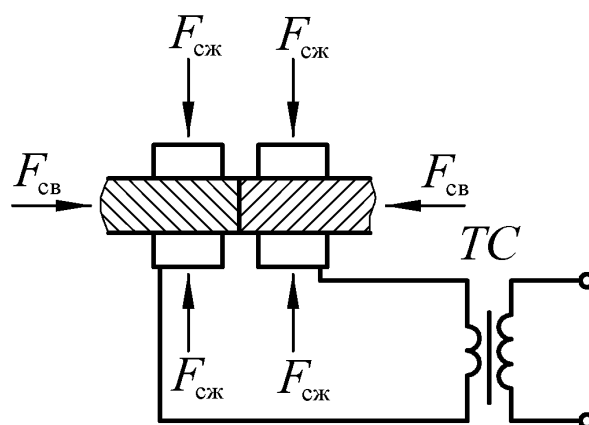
Упрощенная схема контактной стыковой сварки (TC – сварочный трансформатор)
